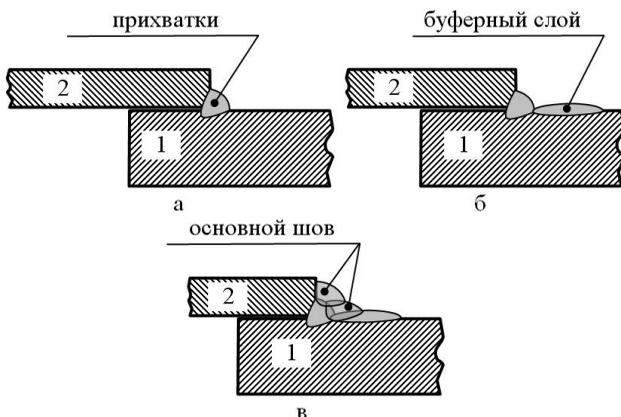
Последовательность выполнения швов при сварке накладки (2) и стенки корпуса опоры морской платформы (1)
